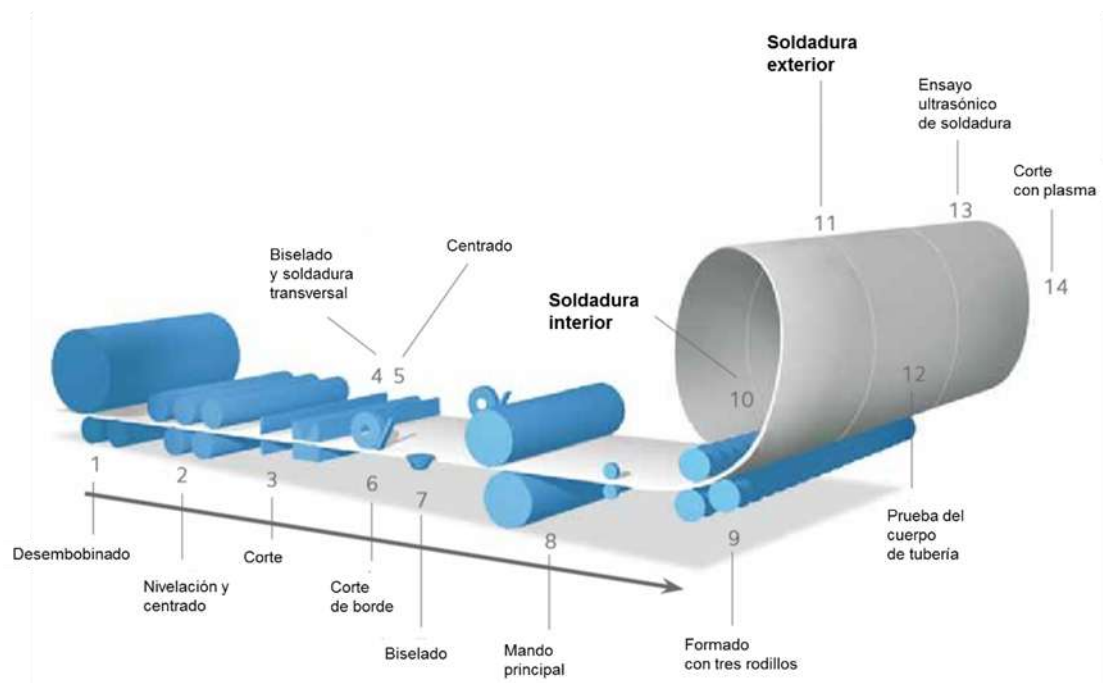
Esquema de soldaduras interior y exterior en producción de tubería (19)
